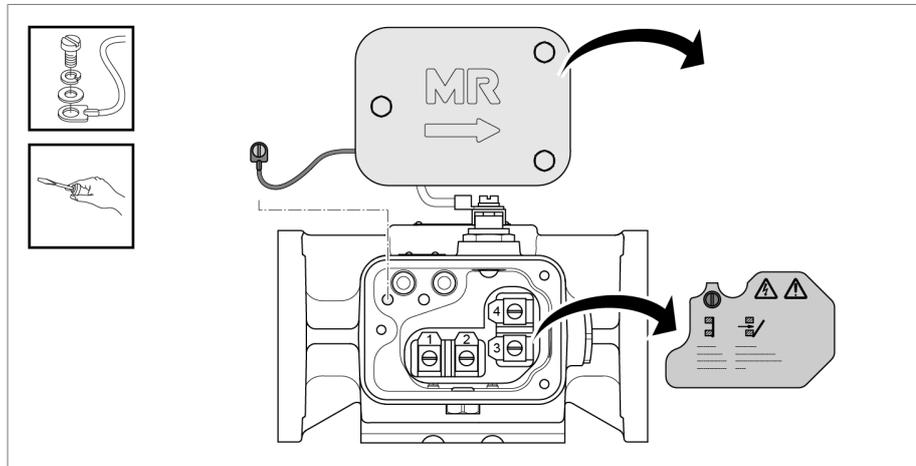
Couvercle du boîtier des bornes et couvercle de protection
